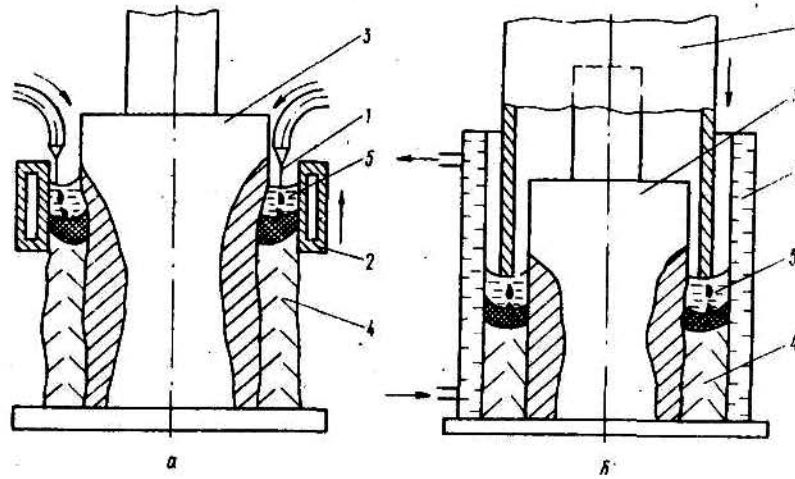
Електрошлакове наплавлення циліндрової поверхні шийок колінчастого валу проволоками (позначення ті ж, що на рис. 1.5.)
